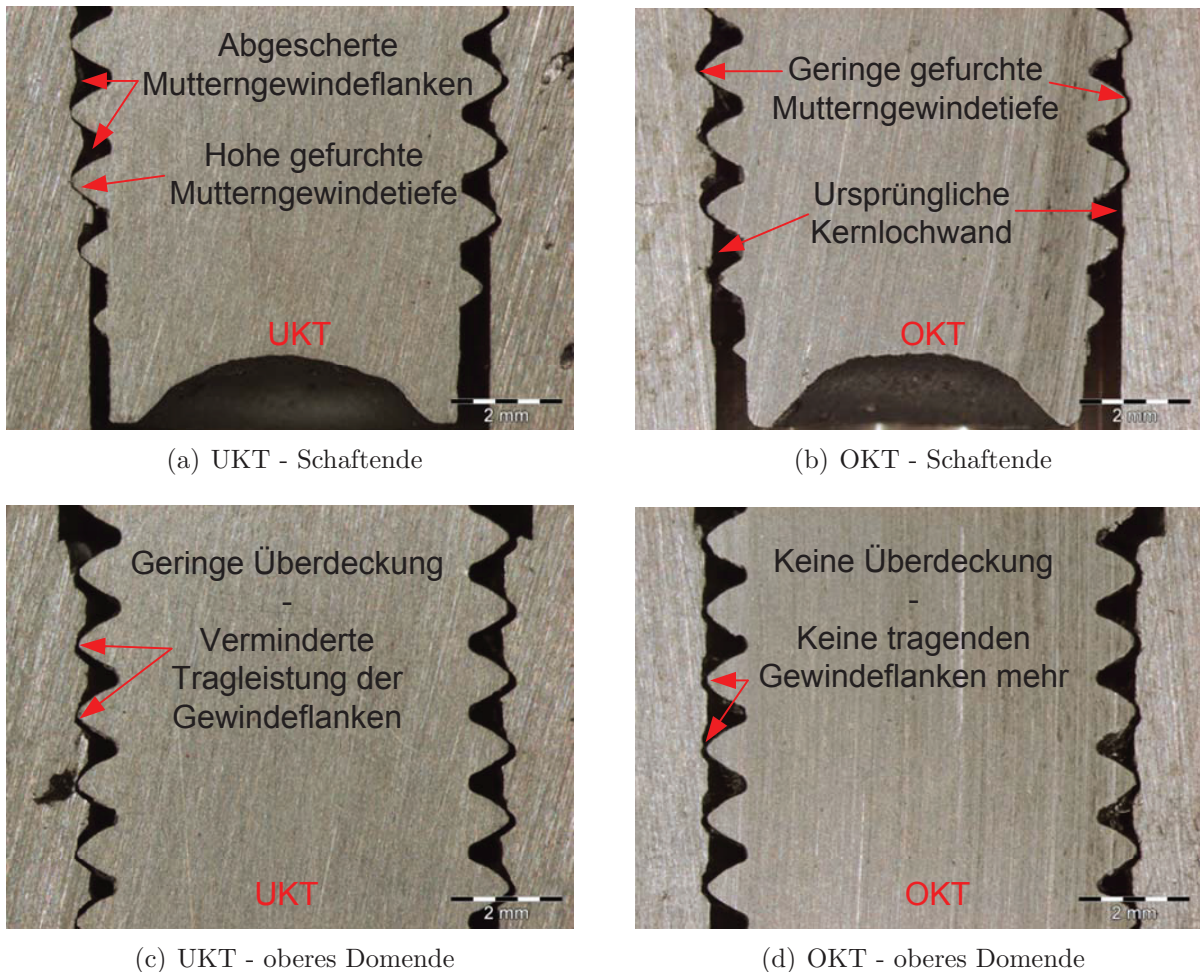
Gewindeüberdeckung von Schrauben- und Mutterngewinde bei UKT und OKT im verschraubten Zustand
